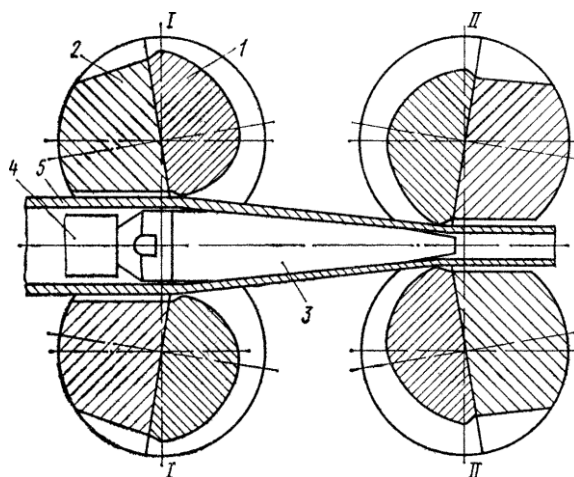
Схема процесса холодной прокатки труб: I-I—крайнее, левое положение валков; II-II— крайнее правое положение валков; 1—рабочая часть валка; 2—валок; 3—оправка; 4—стержень оправки; 5—прокатываемая труба.
